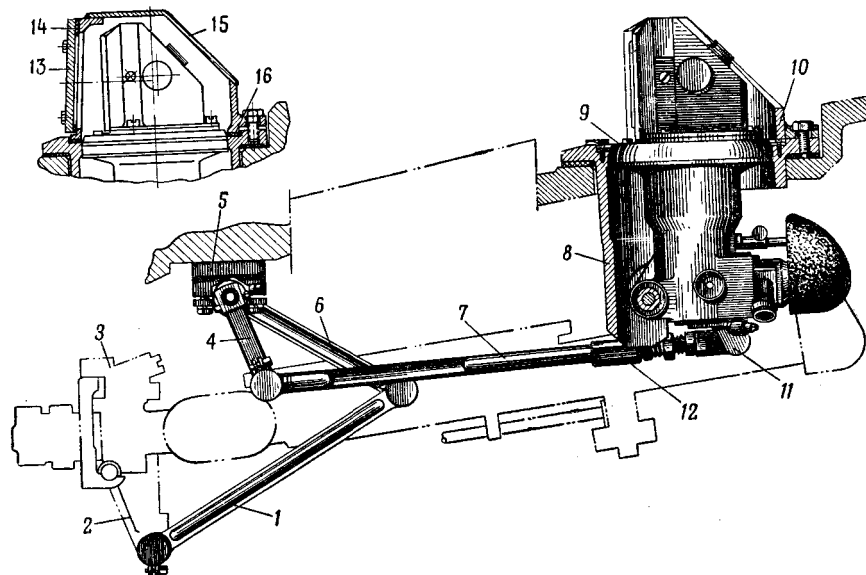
Установка прицела ТПН-1-41-11 в танке:
